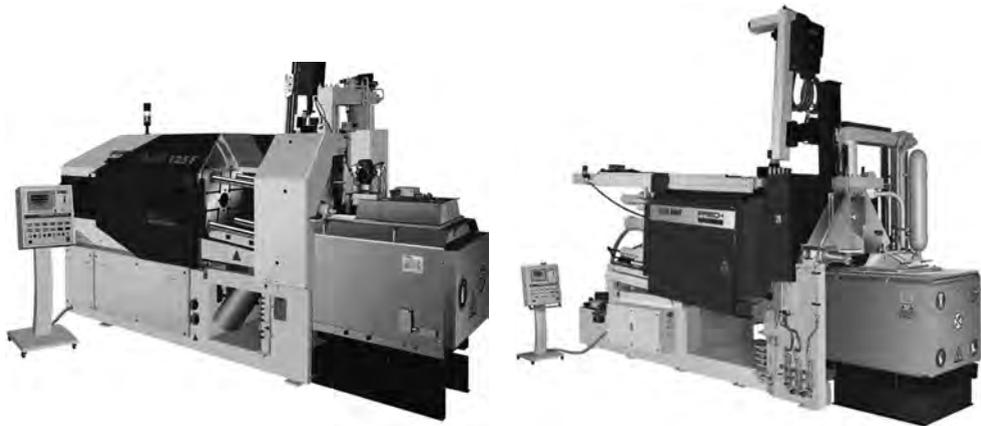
Warmkammer-Druckgießmaschinen DAW 125 F mit einer Formschließkraft von 1250 kN für den Zinkdruckguss und DAM 500 F mit einer Formschließkraft von 5800 kN für den Magnesiumdruckguss (Oskar Frech GmbH & Co. KG)
